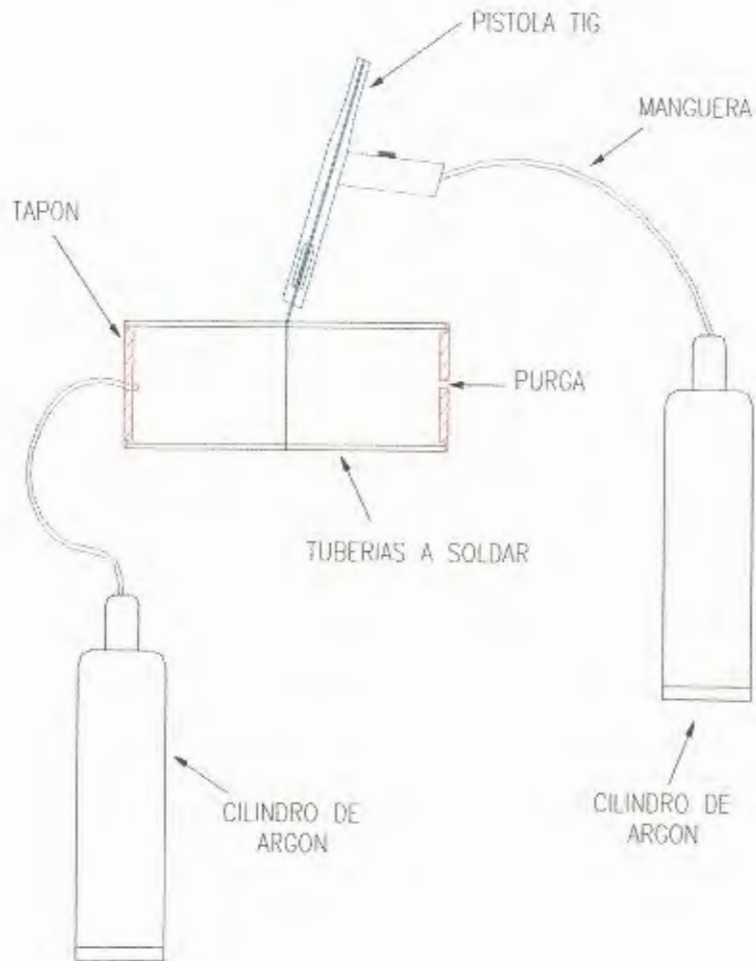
Soldadura de tuberías con proceso TIG barrido interno.
